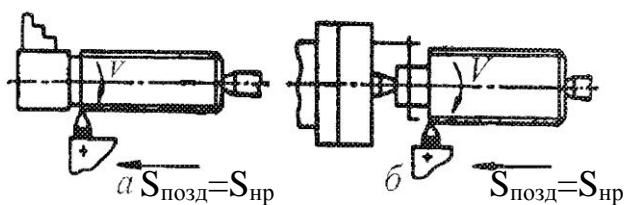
Схеми нарізування однозахідної (а) і багатозахідної різьб на токарно-гвинторізному верстаті
